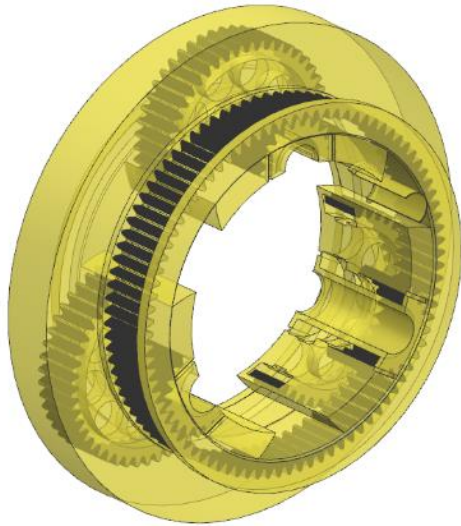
Aanduiding zones in planetaire overbrenging
